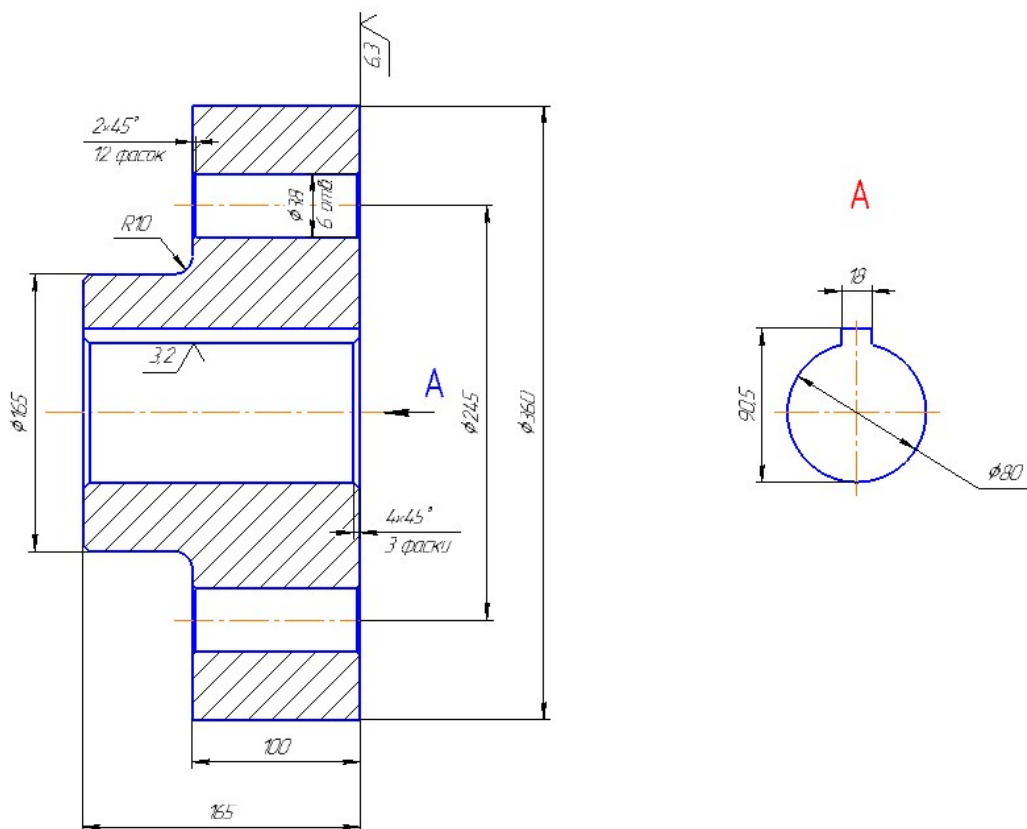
Ескіз деталі "Напівмуфта"
